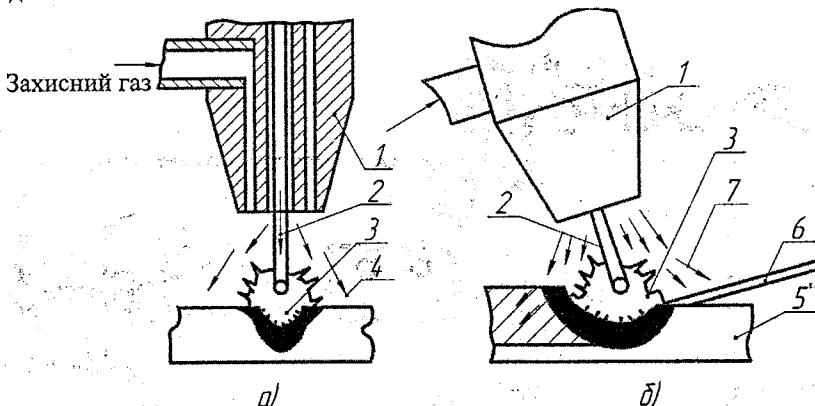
Схема способів заварювання (наплавлення) в середовищі захисних газів
